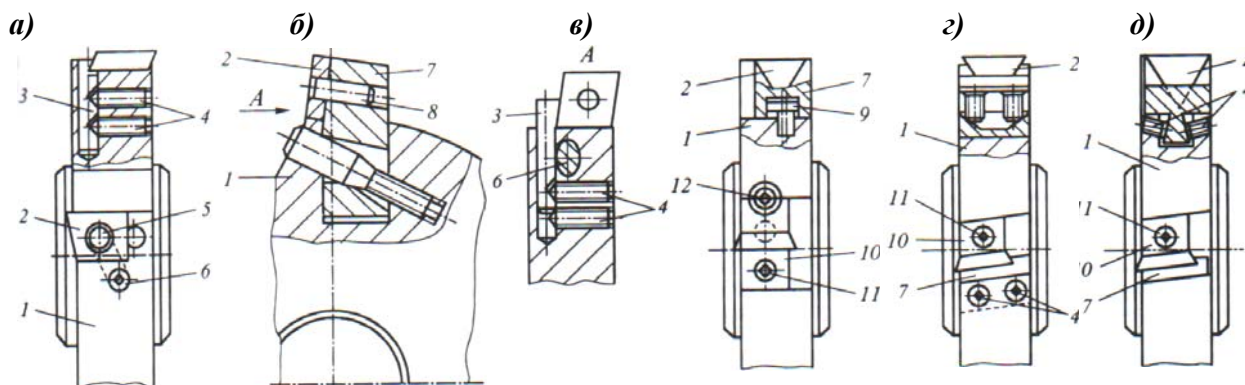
Сборные дисковые фрезы ведущих фирм мира, с регулируемым креплением СМП
